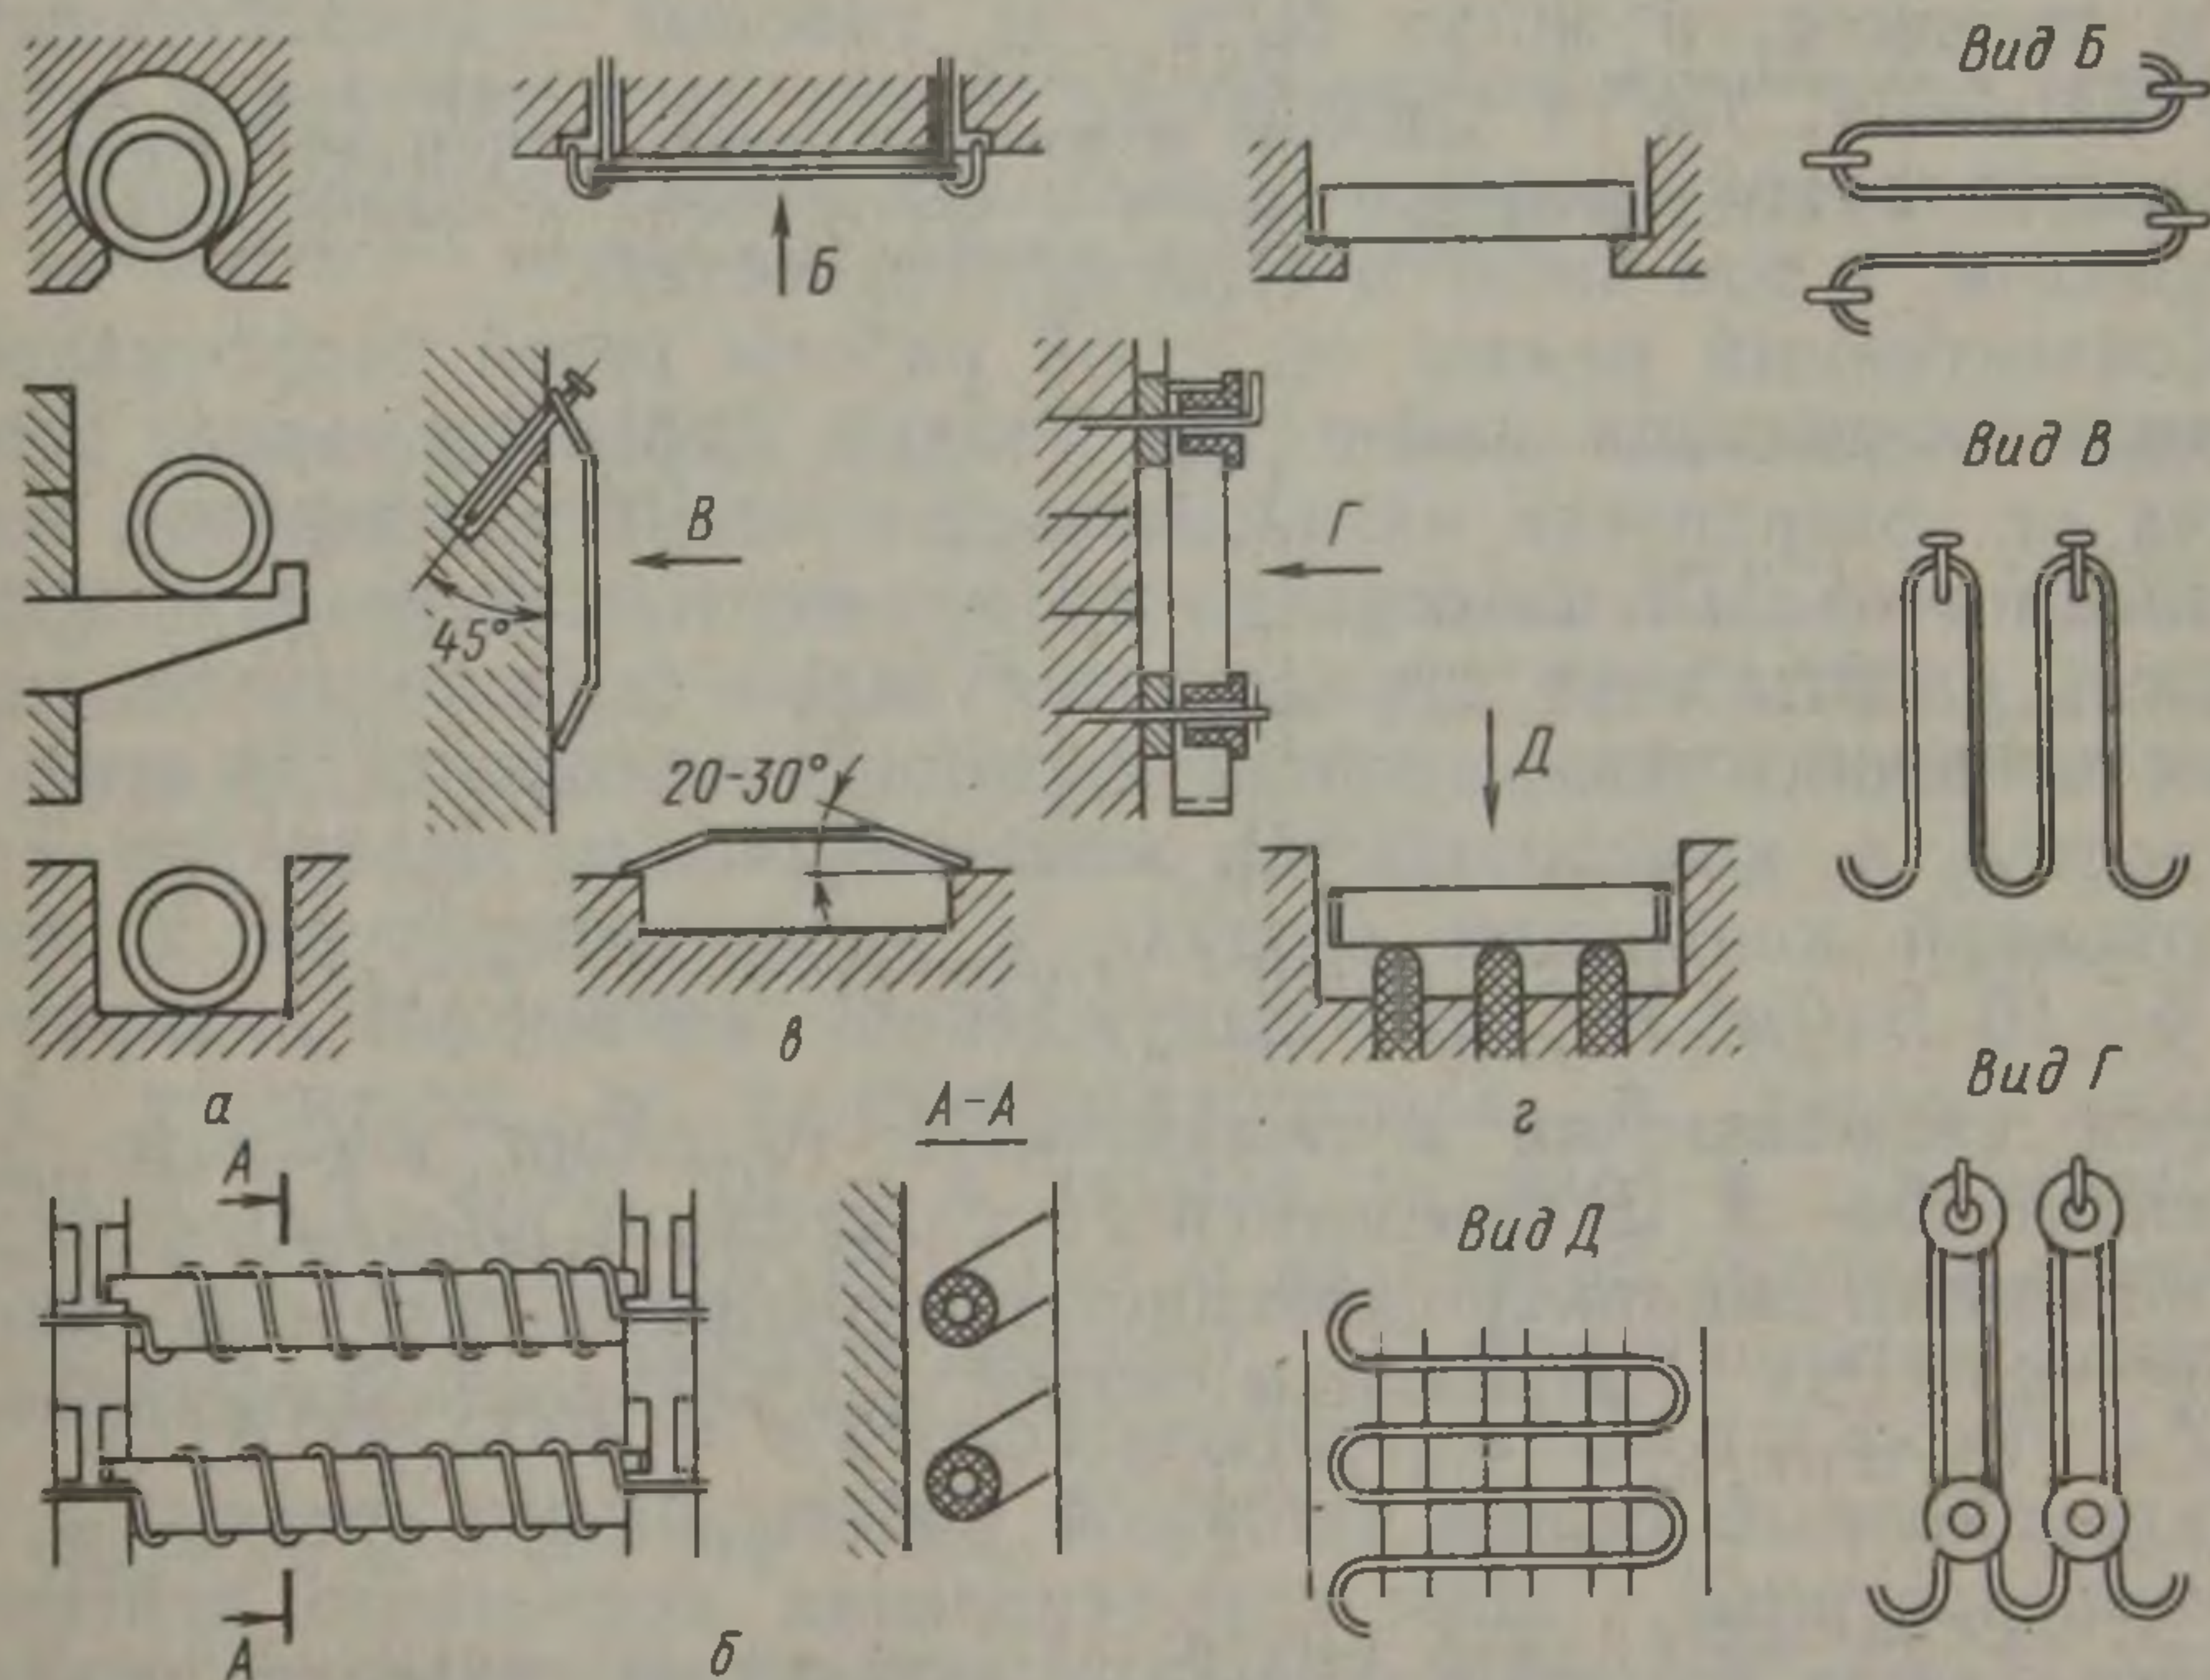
Примеры конструкции и крепления нагревателей:
